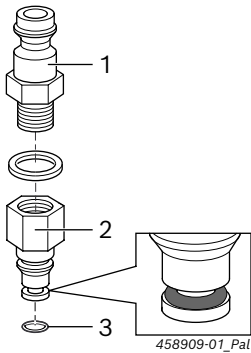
Montage Rücklaufadapter 1 687 016 138
